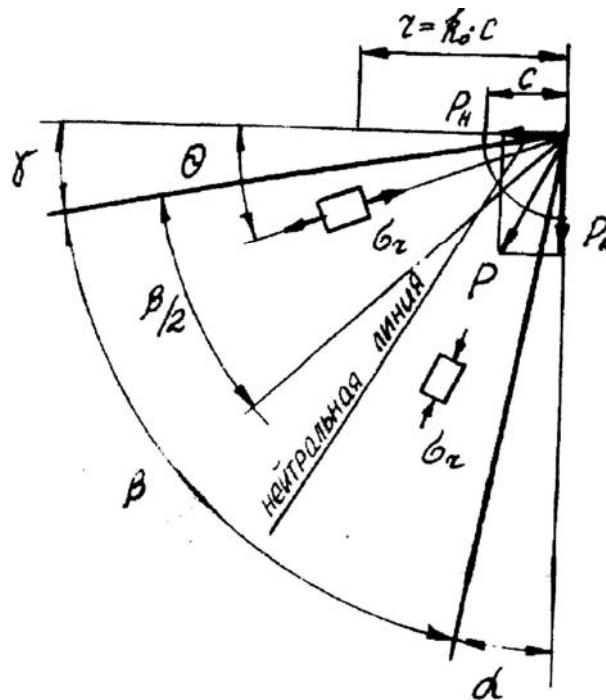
Схема расчета хрупкой прочности режущей кромки чернового резца оцилиндровочного станка
